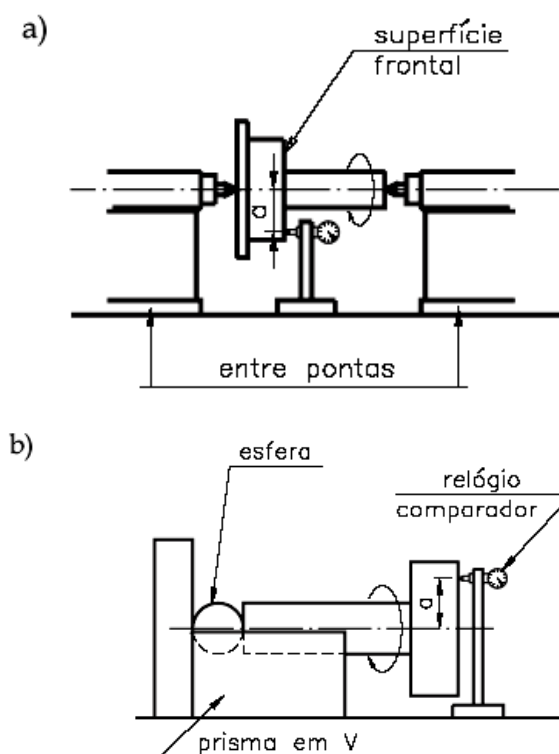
Desenho representativo do sistema de medição do desvio do batimento axial.
